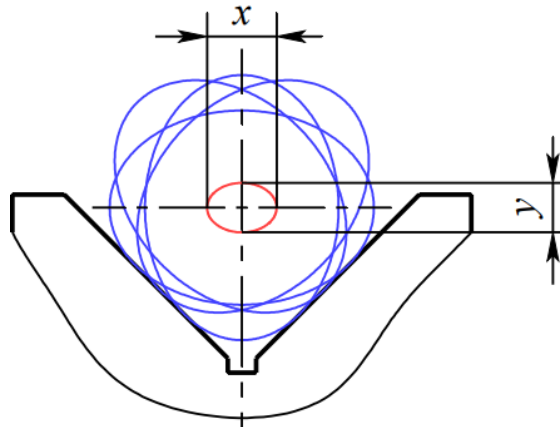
Вплив похибки форми заготовок на їх положення в призмі
